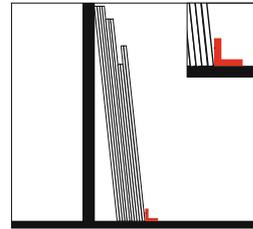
i resti di lamiera appoggiati alle pareti possono essere stabilizzati con un ferro ad angolo fissato al suolo.
